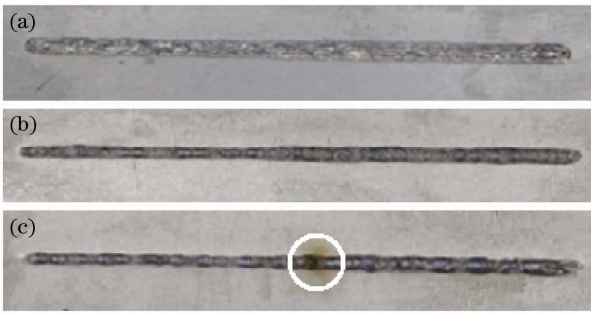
焊缝背面照片。(a)焊缝均匀;(b)焊缝不均匀;
